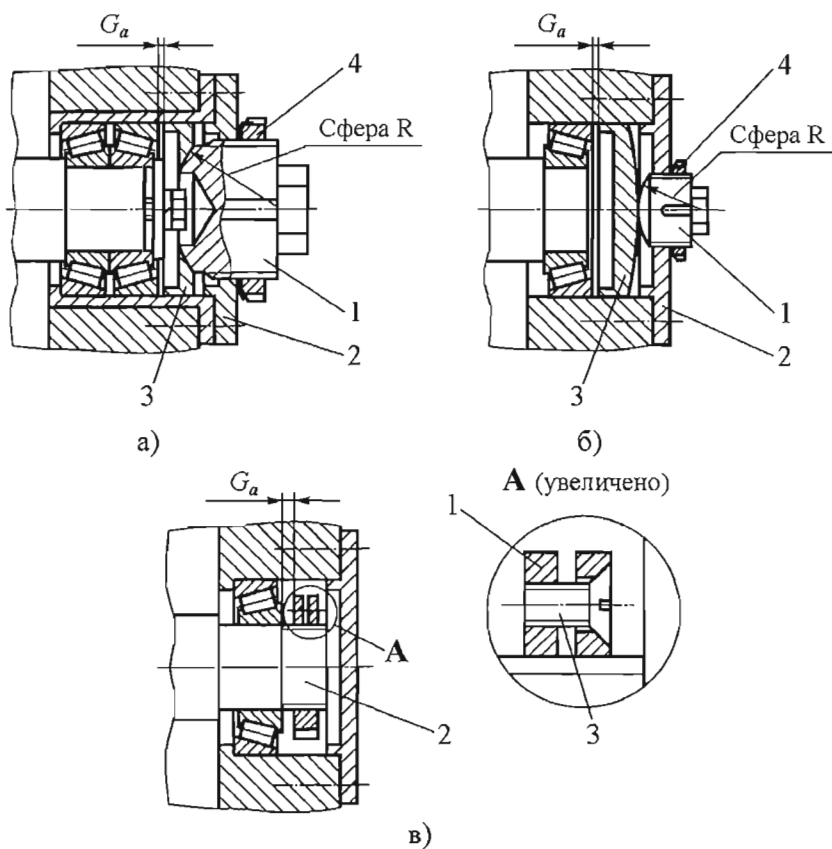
Конструкции подшипниковых узлов, регулируемых резьбовыми деталями
